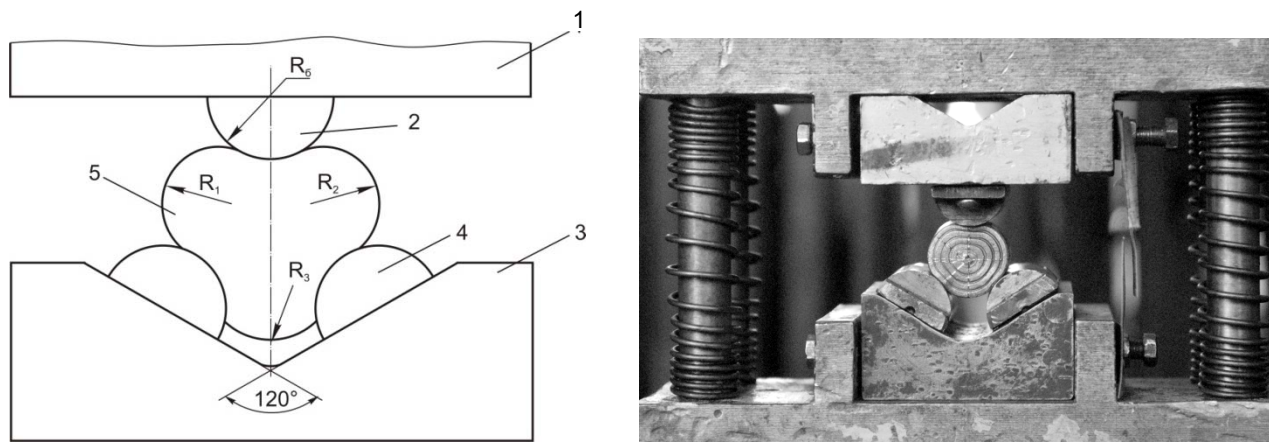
Обжатие заготовки комбинированными профилированными бойками:
